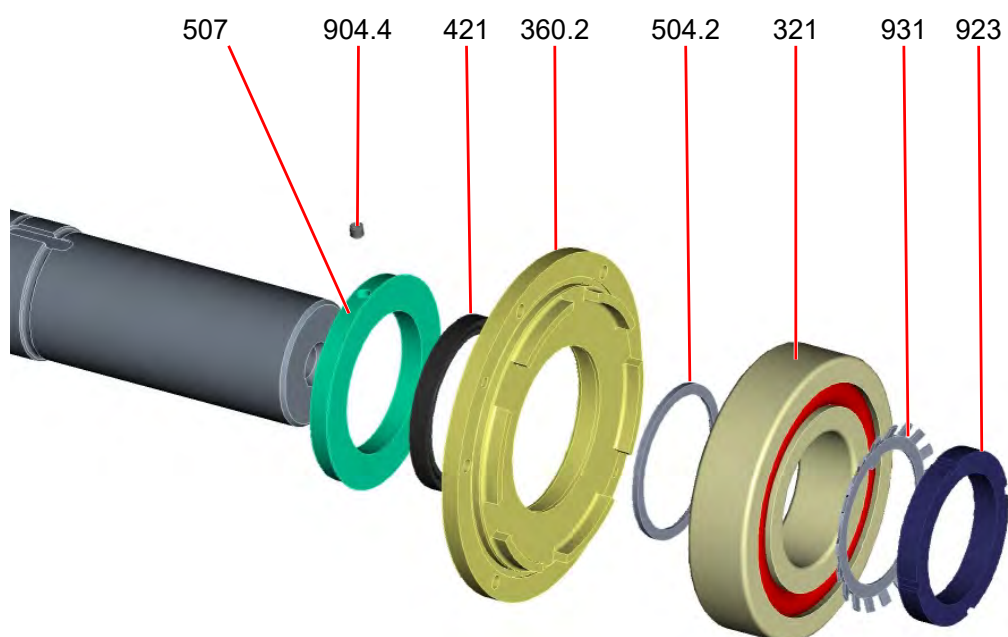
Замена подшипниковой опоры — ASP с платформой
